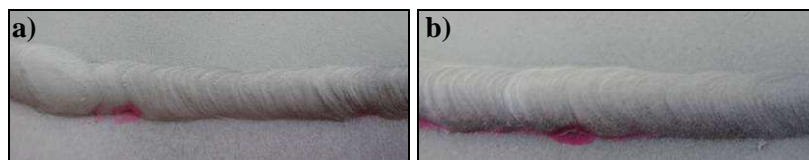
Ensaio de LP após o 20º ciclo de simulação de Fadiga Térmica. a) Soldada com eletrodo AWS E 309MoL-16. b) Soldada com eletrodo AWS E 316L-17
